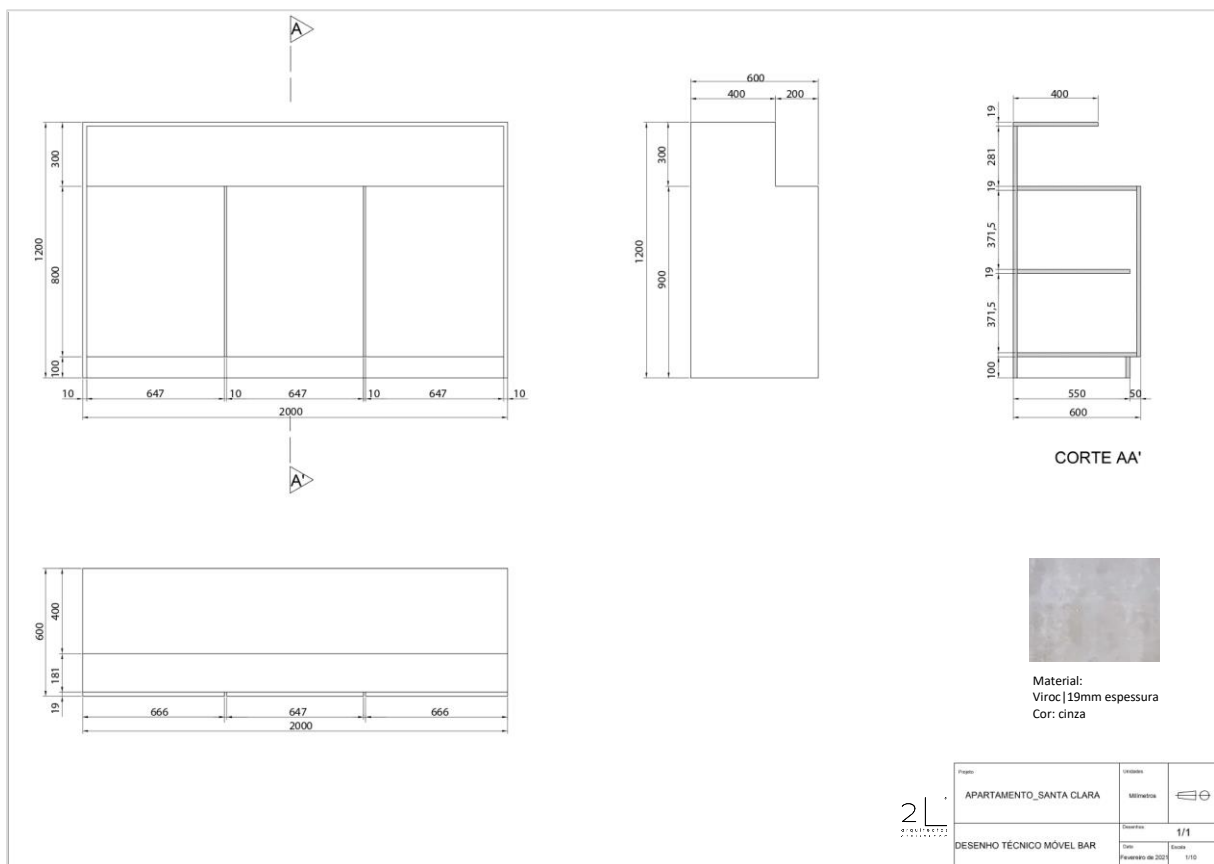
Desenho técnico móvel-bar. Fonte: autora
